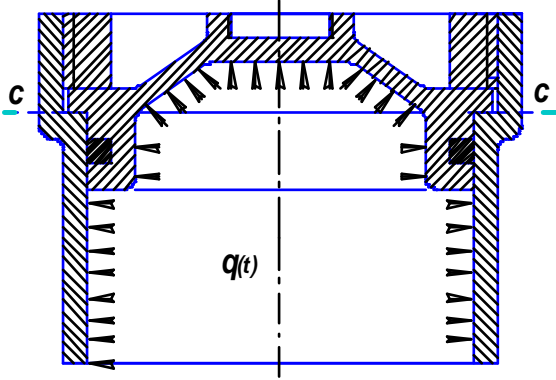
Эскиз резьбового соединения цилиндра под давлением
